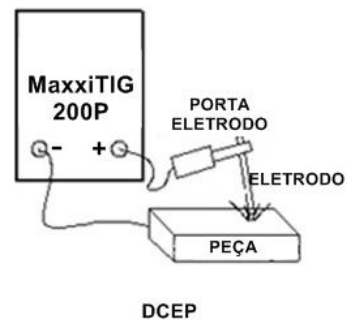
Conexão positiva para soldagem com eletrodo revestido
